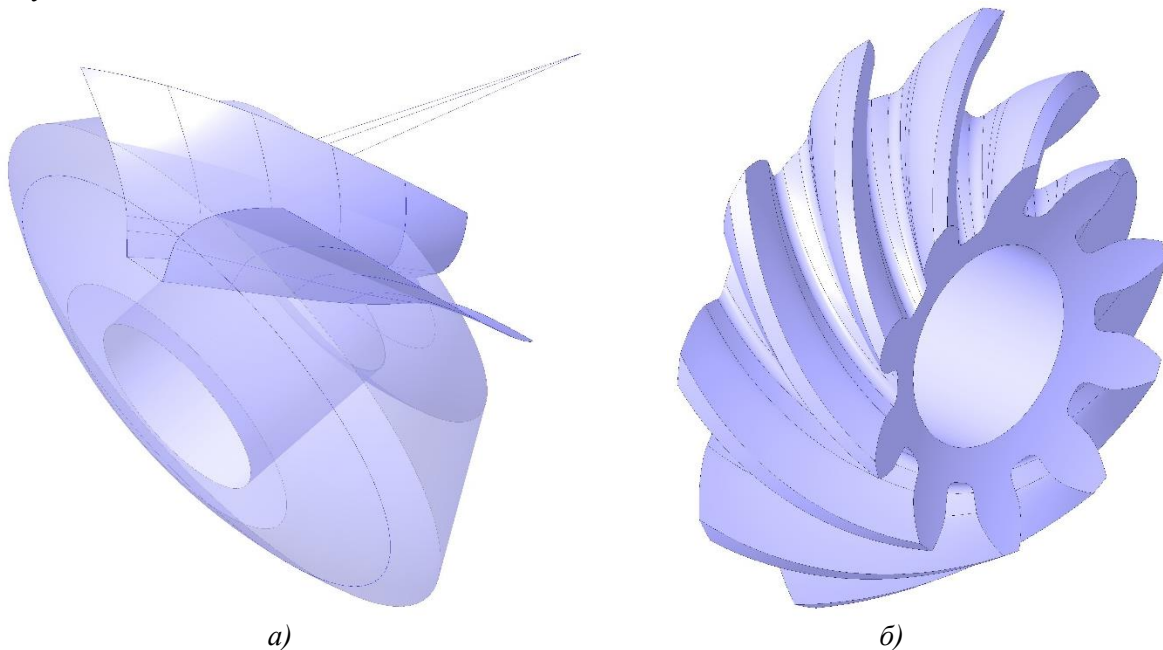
Тримірна модель конічного зубчатого колеса із круговим зубом
